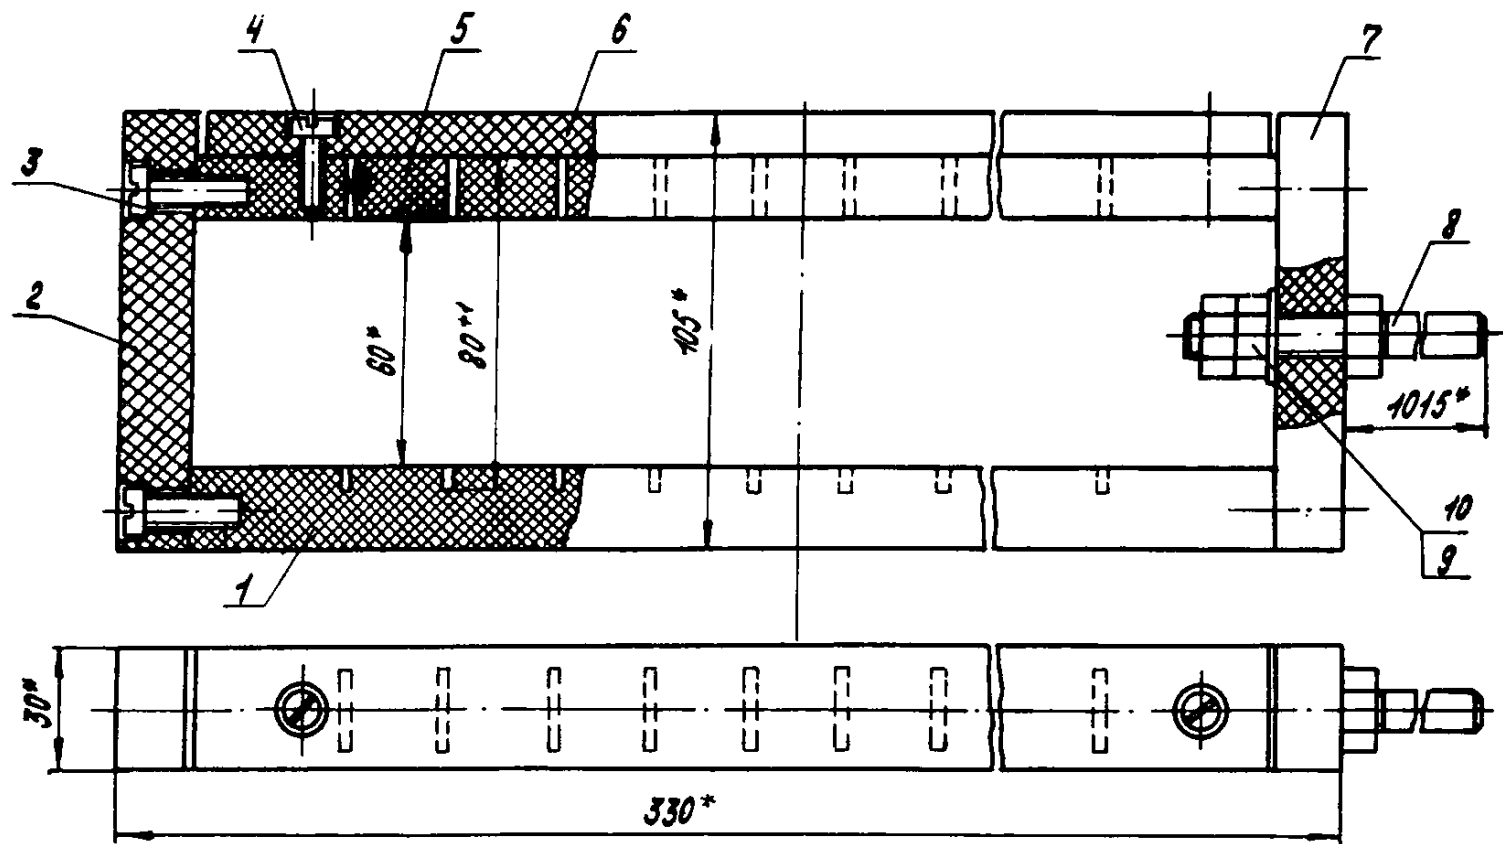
Кассета для установки контрольных образцов через задвижку (сборочный чертеж):
